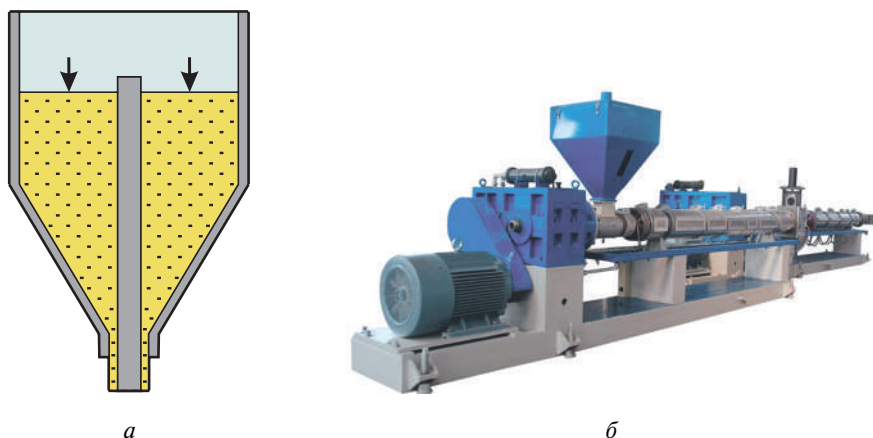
Схема устройства для получения трубчатых заготовок методом экструзии (а); внешний вид экструдера (б)
